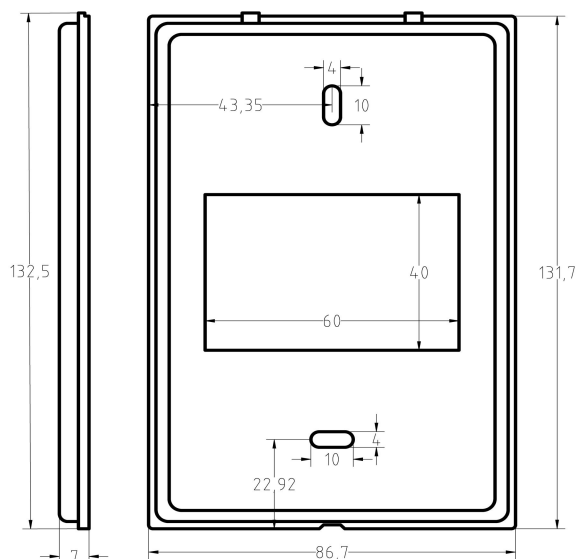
Dimensões da tampa traseira do produto, em milímetros (mm).
